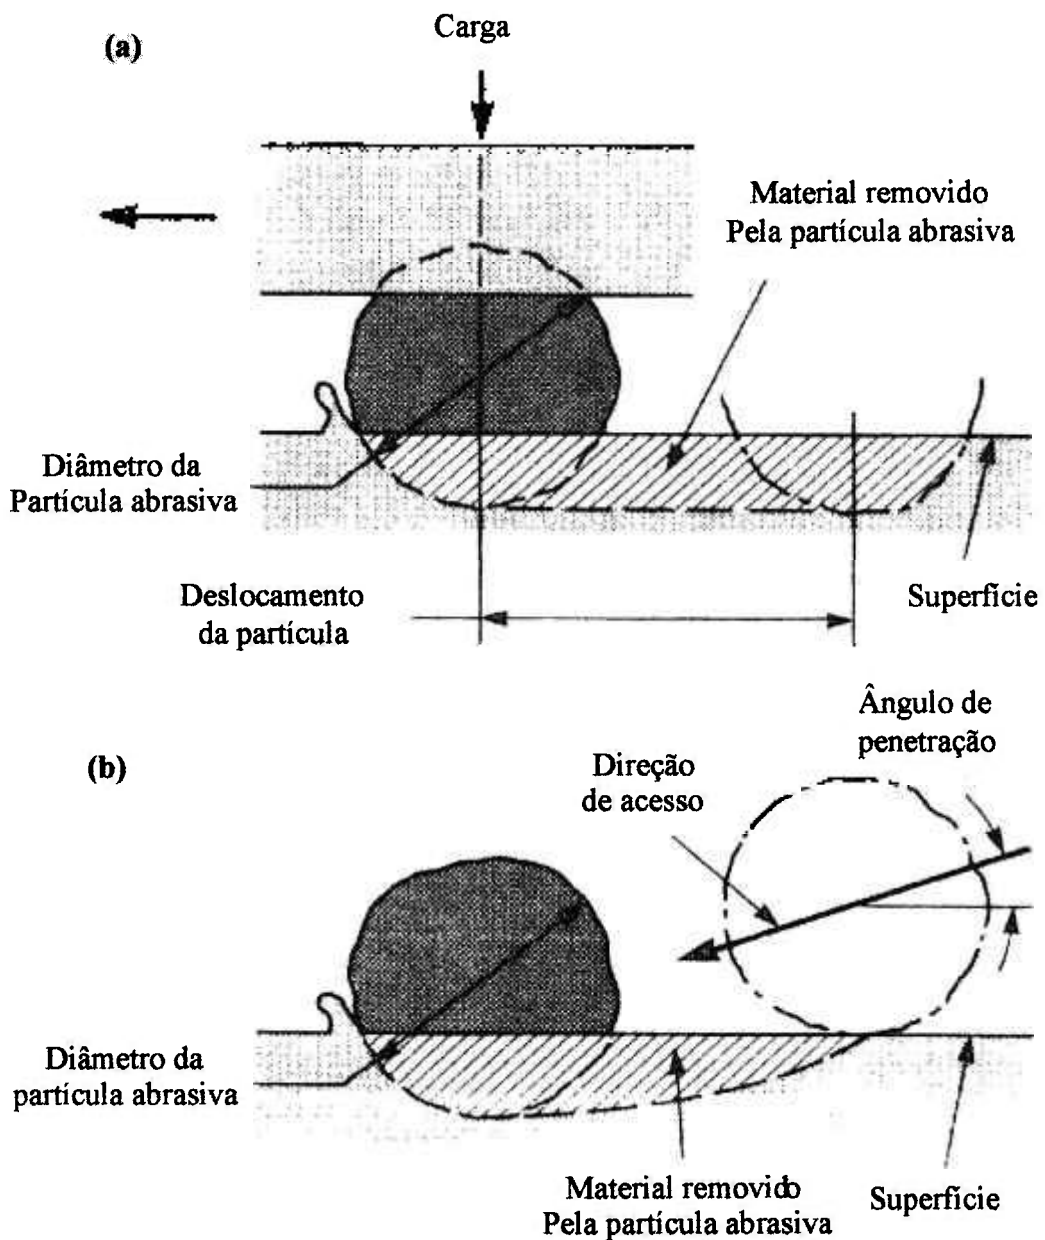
Representação do mecanismo de abrasão (a) observação de partícula sobre pressão, característica do processo de usinagem, (b) ação de uma partícula suspensa que penetra através da superfície
